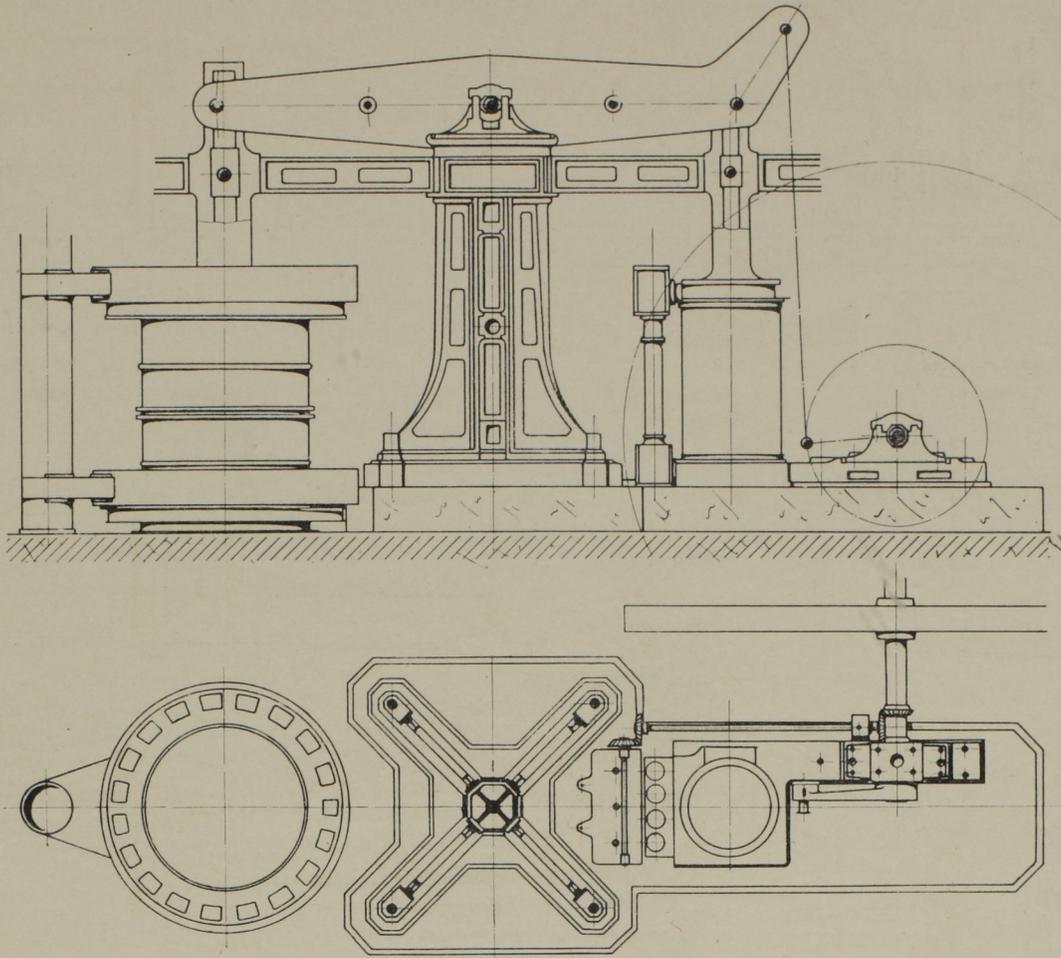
Seitenansicht und Grundriss der Gebläsemaschine. Massst. 1:20.
